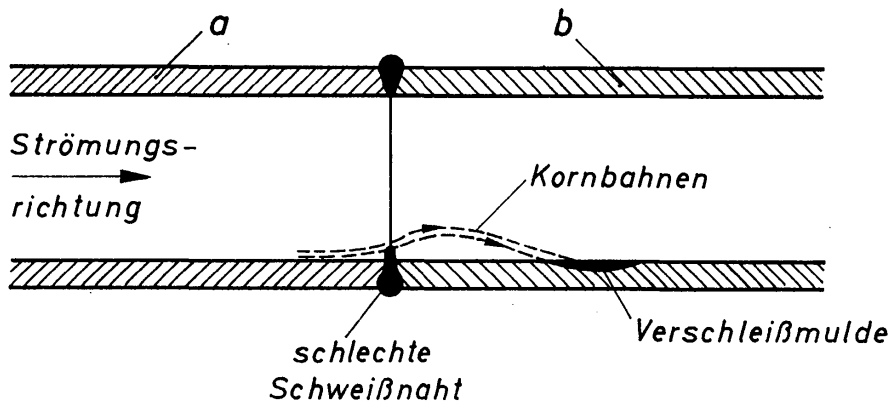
Verschleißmulde hinter einer mangelhaft ausgeführten Schweißnaht
